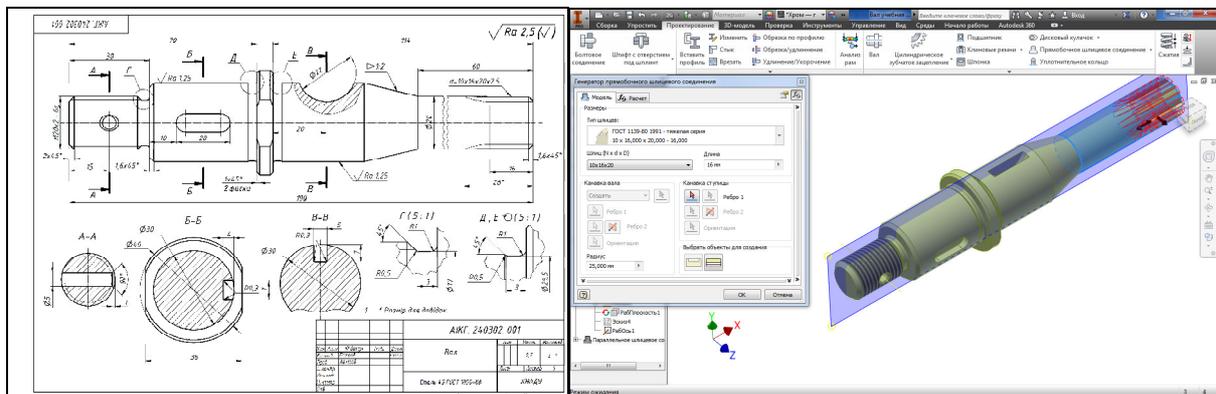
Робочий кресленик деталі типу «Вал» та моделювання шліців
